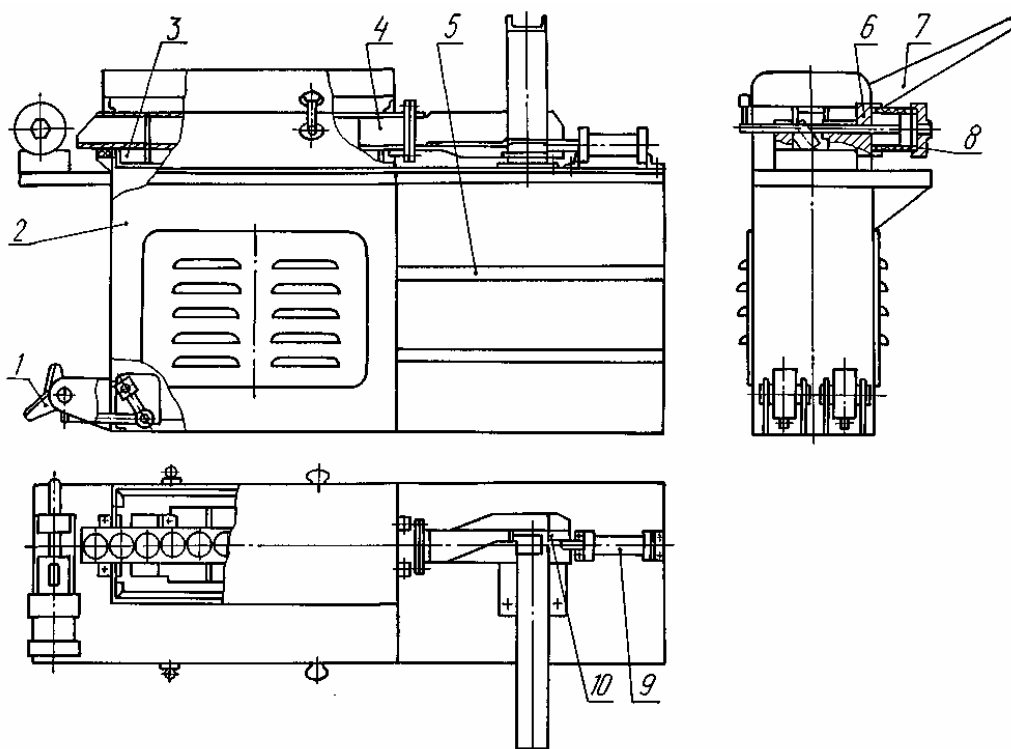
Схема станда для сборки шатунно-поршневых групп: 1 – педальный привод; 2 – корпус; 3 – нагреватель; 4 – лоток; 5 – стеллаж; 6 – прессосборочный механизм; 7 – питатель; 8 и 9 – пневмоцилиндры; 10 – отсекабель
